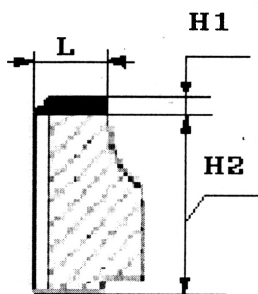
Расположение закаленного и незакаленного ТВЧ слоя на плоской поверхности детали ступица шестерни: H1 — закаленный слой; H2 — незакаленный слой; L — длина закаленного слоя
